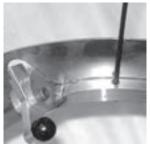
Montieren Sie die Auslöserbaugruppe am Gehäuse.
